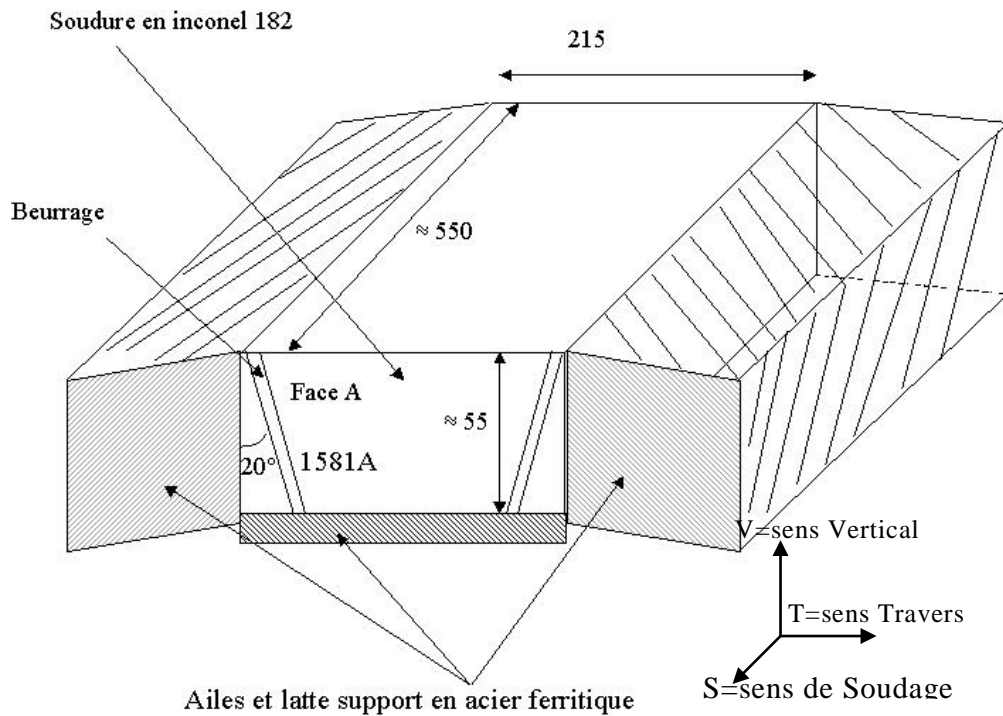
Caractéristiques du moule de soudage en Inconel 182.
